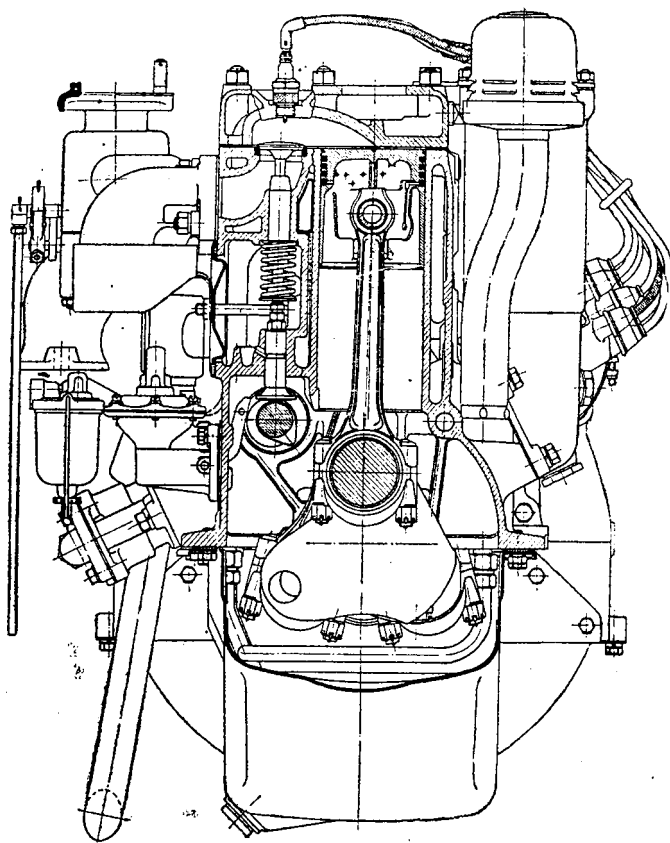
Поперечный разрез шестицилиндрового двигателя по первому цилиндру.
